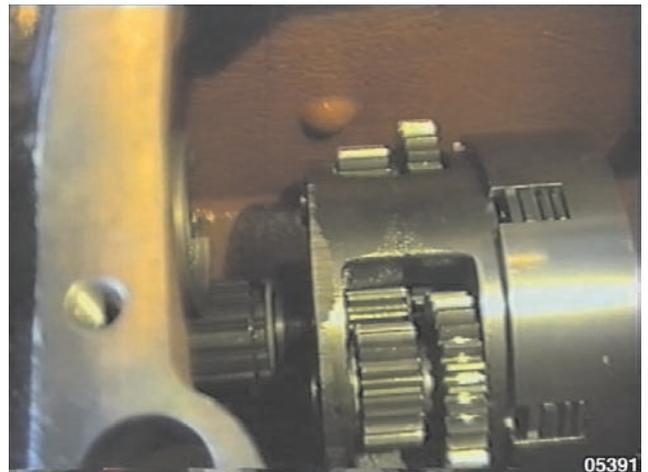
Ensemble Powershift monté dans le carter de boîte.
